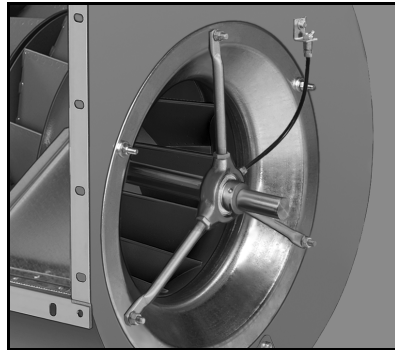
Rillenkugellager mit Streben-Gussgehäuse
